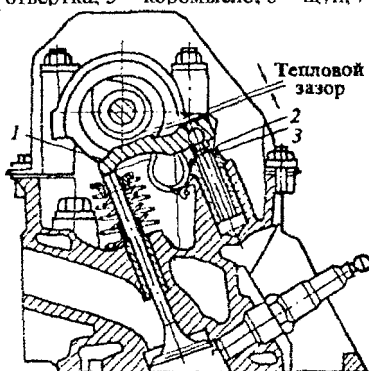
Регулировка тепловых зазоров газораспределительного механизма автомобиля ВАЗ классической компоновки: 1 – коромысло; 2 – регулировочный винт; 3 – контргайка
